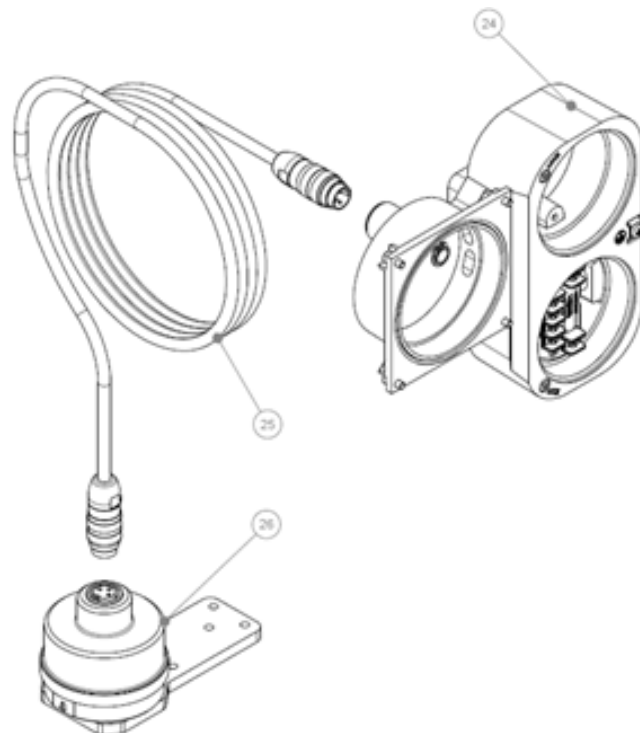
Dibujo explotado del sensor remoto del VVP10.
